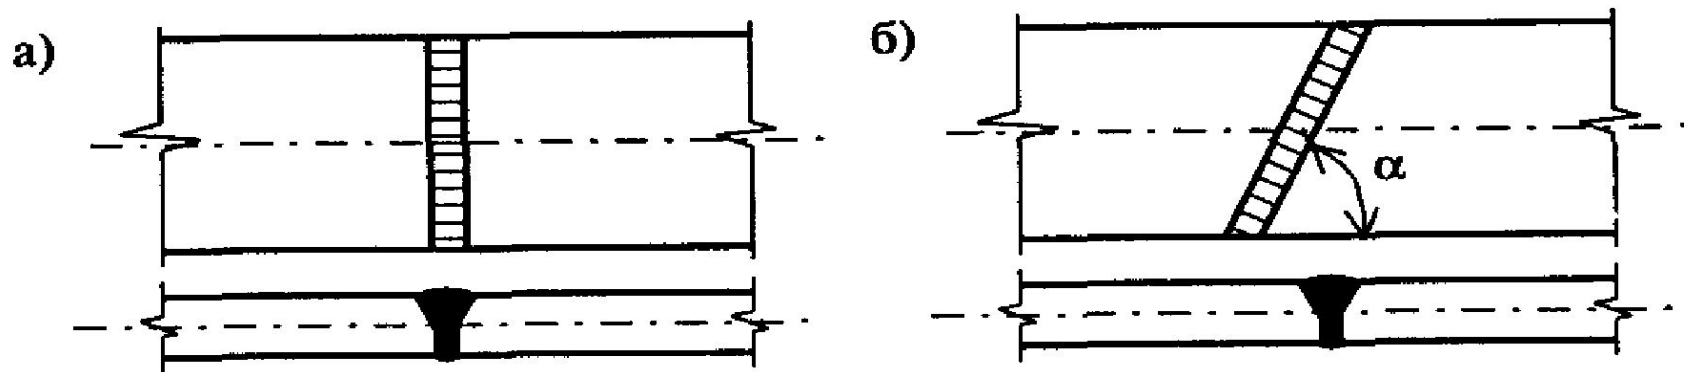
Стыковые сварные соединения: а) прямой стыковой шов;
